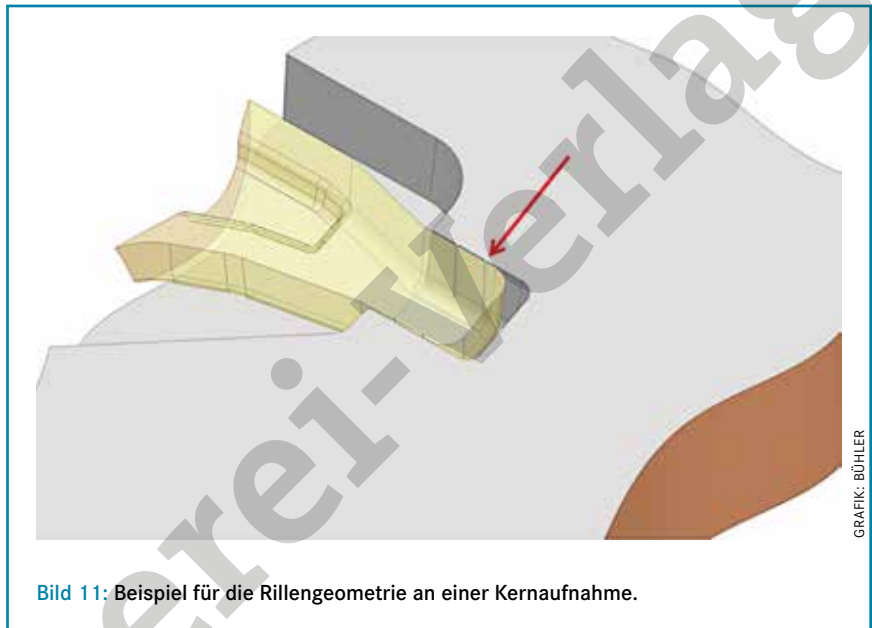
Beispiel für die Rillengeometrie an einer Kernaufnahme.
